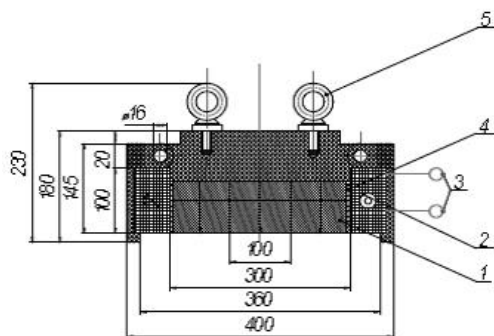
Конструкция КЖ блочного типа для установки над лентой конвейера шириной 400 мм: 1 — блоки ПМ; 2 — обмотка; 3 — выводы обмотки; 4 — рейки деревянные, фиксирующие обмотки и магнитные плиты; 5 — рым-болты для подъема КЖ
